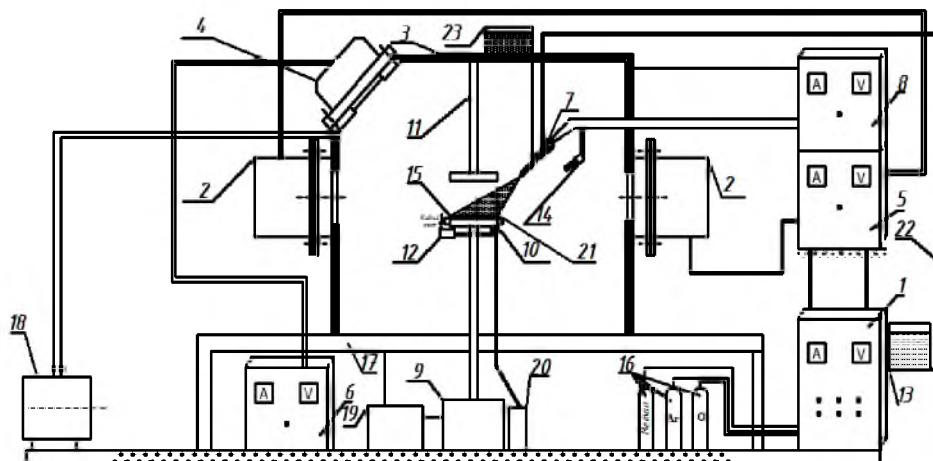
Схема вакуумной установки для формирования наноструктурированных поверхностных слоев из материала с ЭПФ: 1 – блок управления; 2 – источник питания; 3 – сварочный трансформатор; 4 – патрон; 5 – трехроликное приспособление для ППД полученного покрытия; 6 – газопламенная горелка; 7 – устройство для перемещения газопламенной горелки; 8 – устройство для подачи жидкого азота; 9 – порошковый дозатор; 10 – пирометр; 11 – система подачи газов; 12 – задняя бабка; 13 – электродвигатель; 14 – шкивы для передачи крутящего момента от электродвигателя 13 на патрон 4; 15 – рама; 16 – обрабатываемая деталь; 17 – вакуумная камера; 19 – вакуумный насос; 20 – технологический модуль для ионной очистки поверхности детали; 21 – смотровые окна
